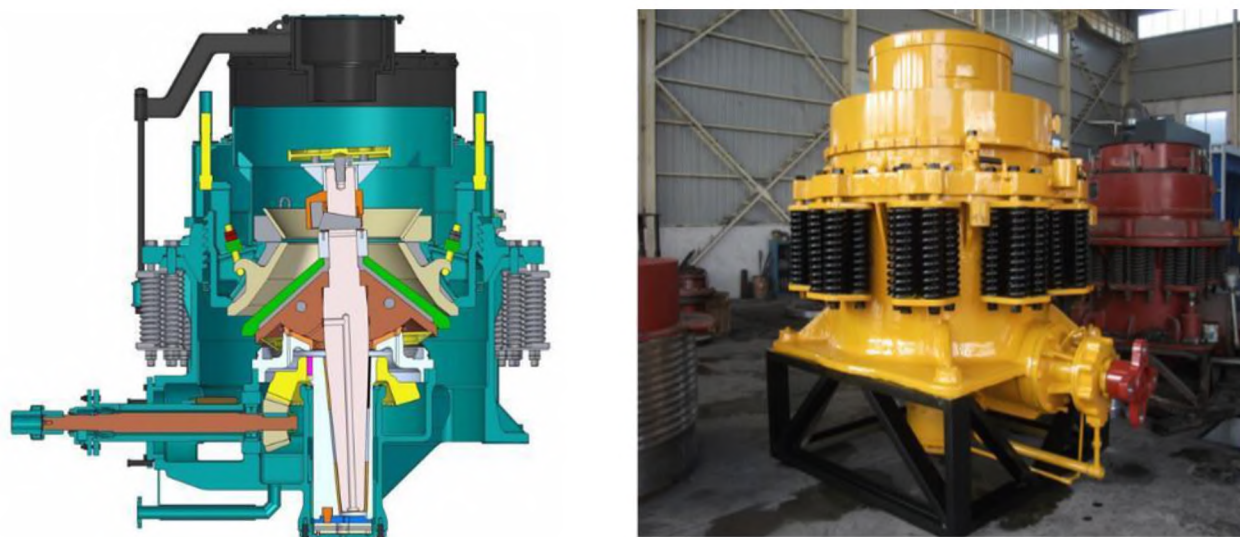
Конусная дробилка среднего дробления: конструкция и внешний вид
